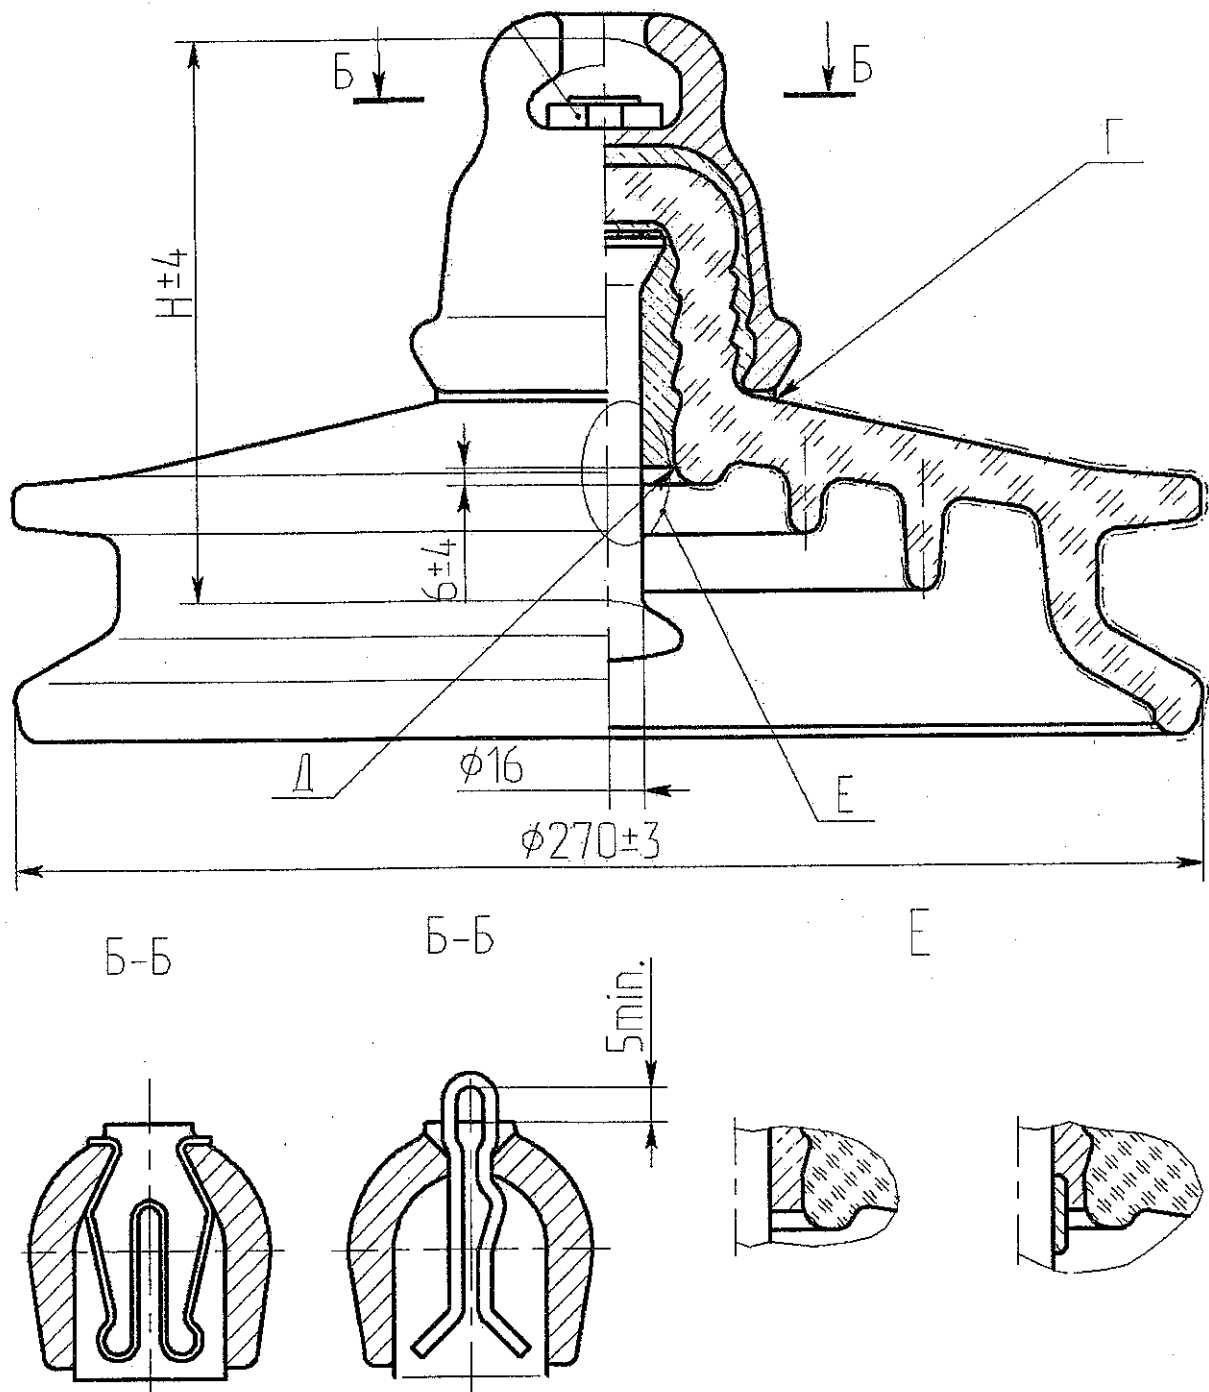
Габаритные, присоединительные и установочные размеры изолятора ПСД 70Е
